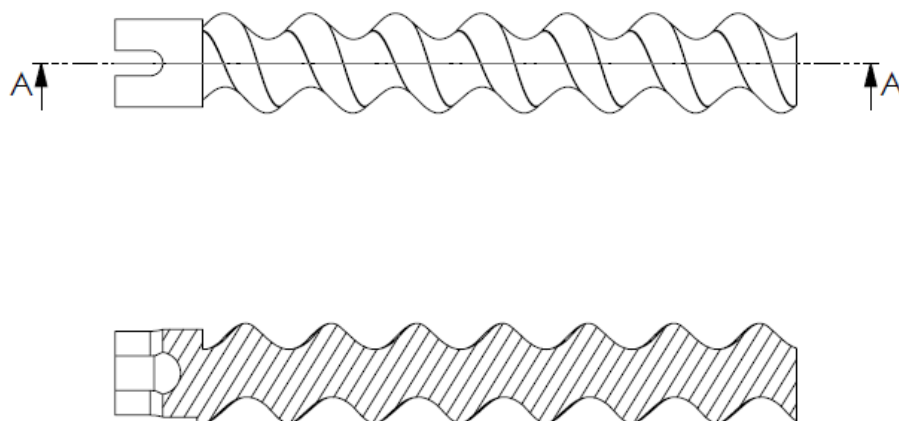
Конструктивна схема ротора гвинтового вузла
